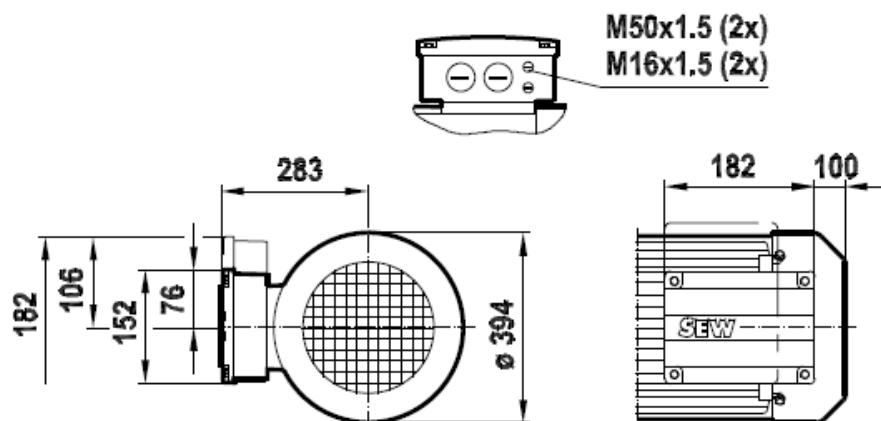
Desenho técnico do motor elétrico DRN200L.
